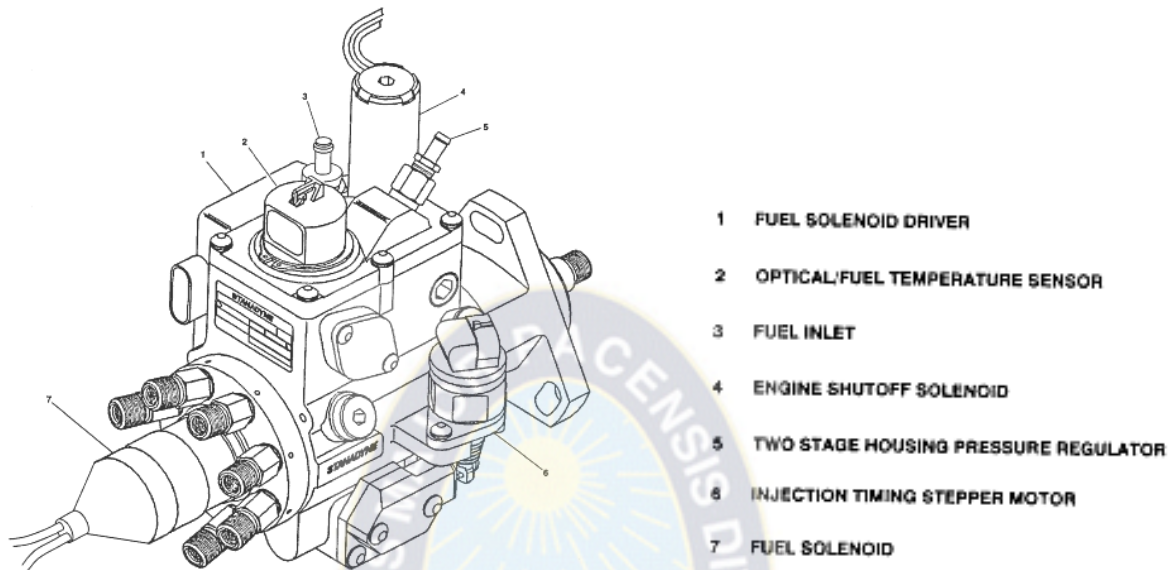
Solenoide de apagado de motor (General Motors Corporation)
